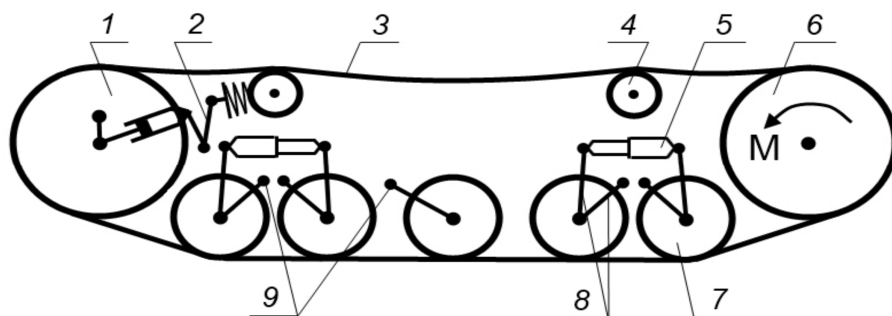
Схема гусеничного движителя трактора «Беларус-2103»: 1 – направляющее колесо; 2 – механизм натяжения гусеницы; 3 – гусеница; 4 – поддерживающий каток; 5 – гидроамортизатор; 6 – ведущее колесо; 7 – опорный каток; 8 – балансир; 9 – торсионы
